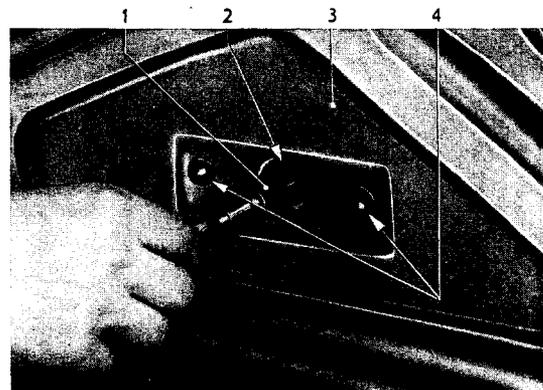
Zusätzliche Schraube für Fensterrahmen am Caravan und Lieferwagen herauserschrauben
